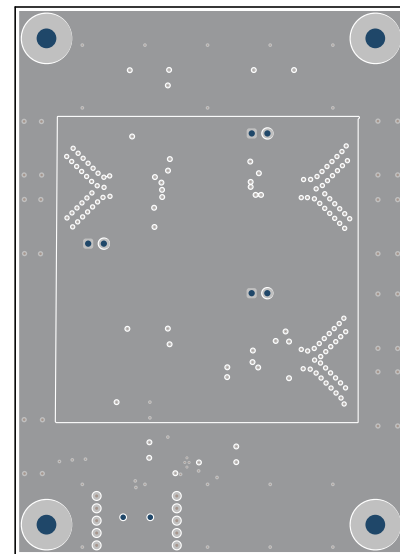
LMK6BEVM の PCB レイアウト例 - 電源層
